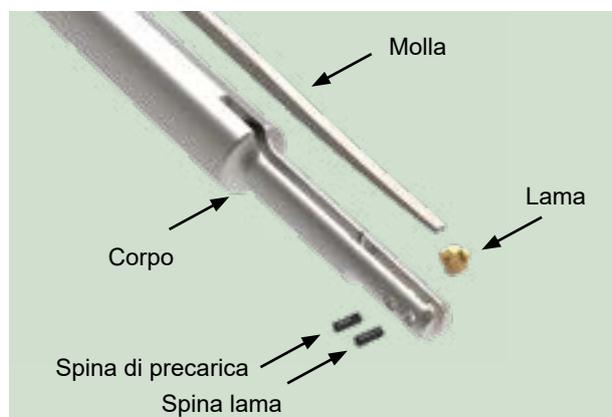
Per cambiare la lama, rimuovere la spina frontale e ruotarla fuori dalla molla.
